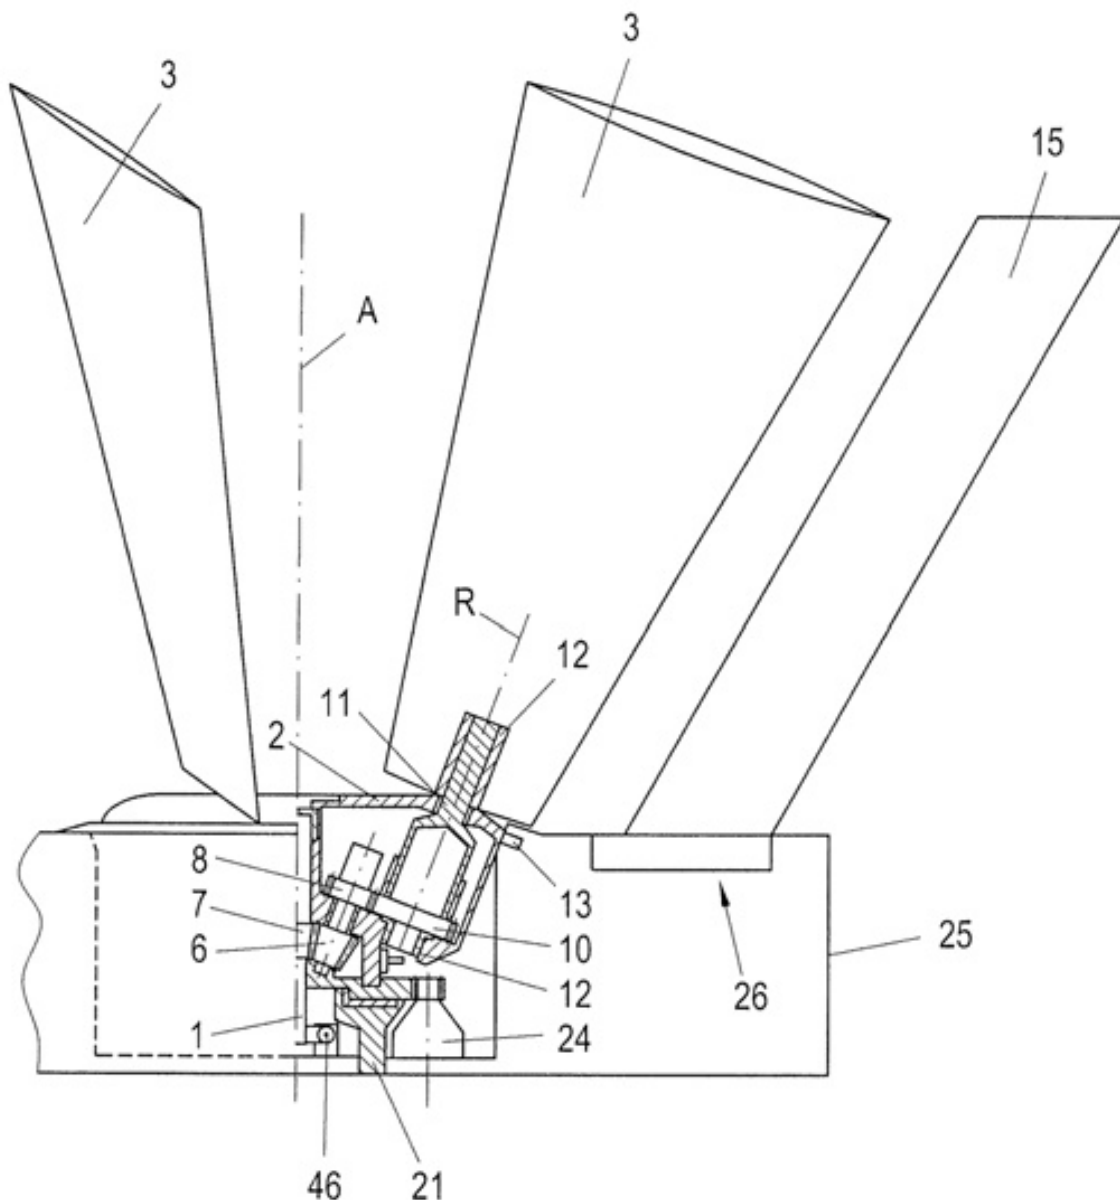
Seitenansicht der Windturbine mit innerem Aufbau der Schaufelverstellung, bei der rechten Laufschaufel 3 sind die Dimensionen einer ohne Verzerrung dargestellt.
